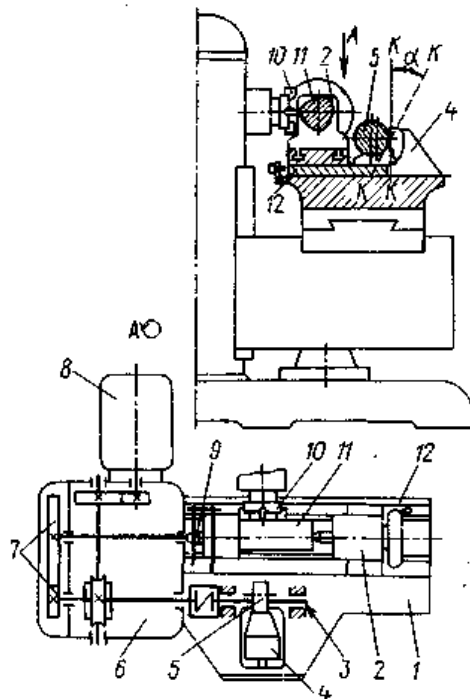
Агрегат для торцевого фрезерування профільних валів
